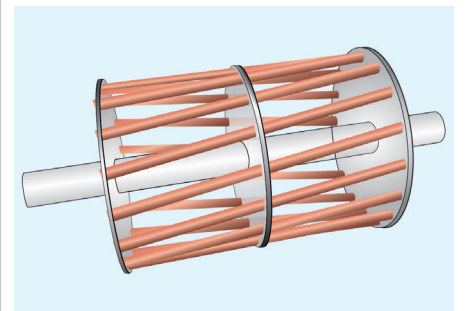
Le rotor à cage d'écurieil de la machine asynchrone, souvent comparé à une roue de hamster.
